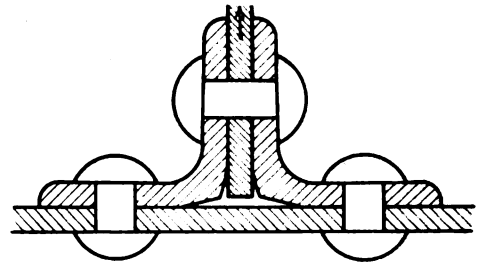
Formänderung einer genieteten Winkelverbindung bei auftretender Beanspruchung
